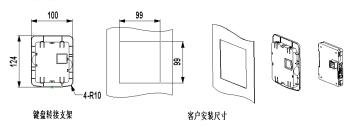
300 系列 钣金结构外型尺寸及安装尺寸示意图
